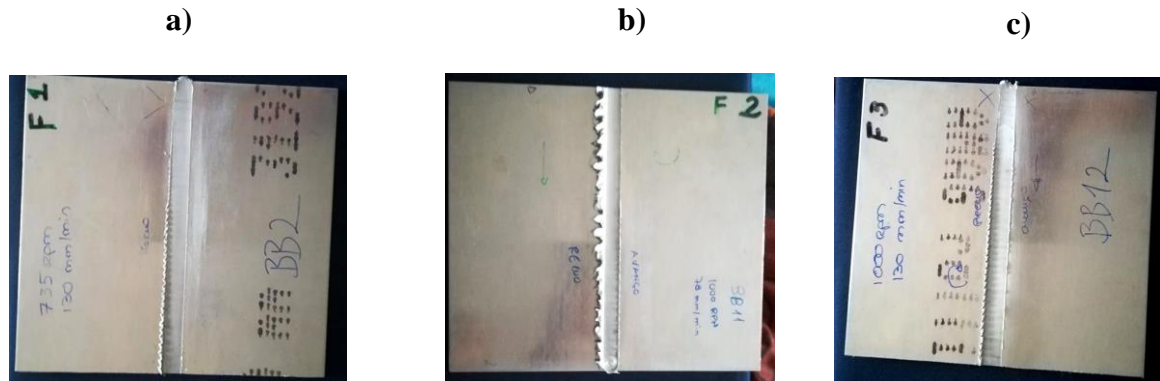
Placa 2 com junta soldada por MIG.
